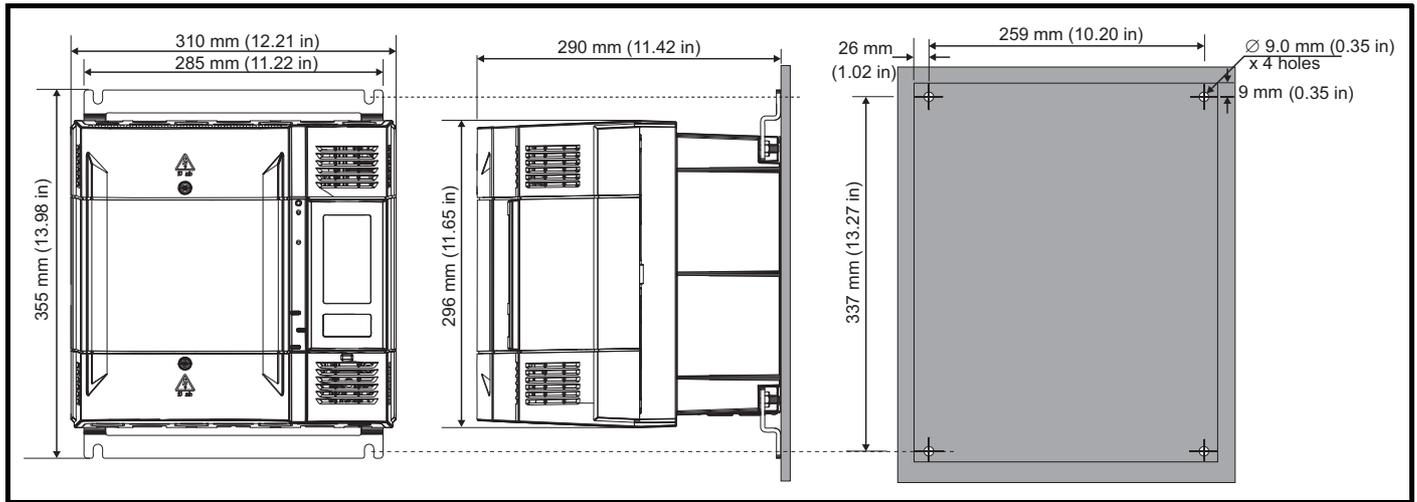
Unidrive M / Unidrive HS 11 型的表面安装
